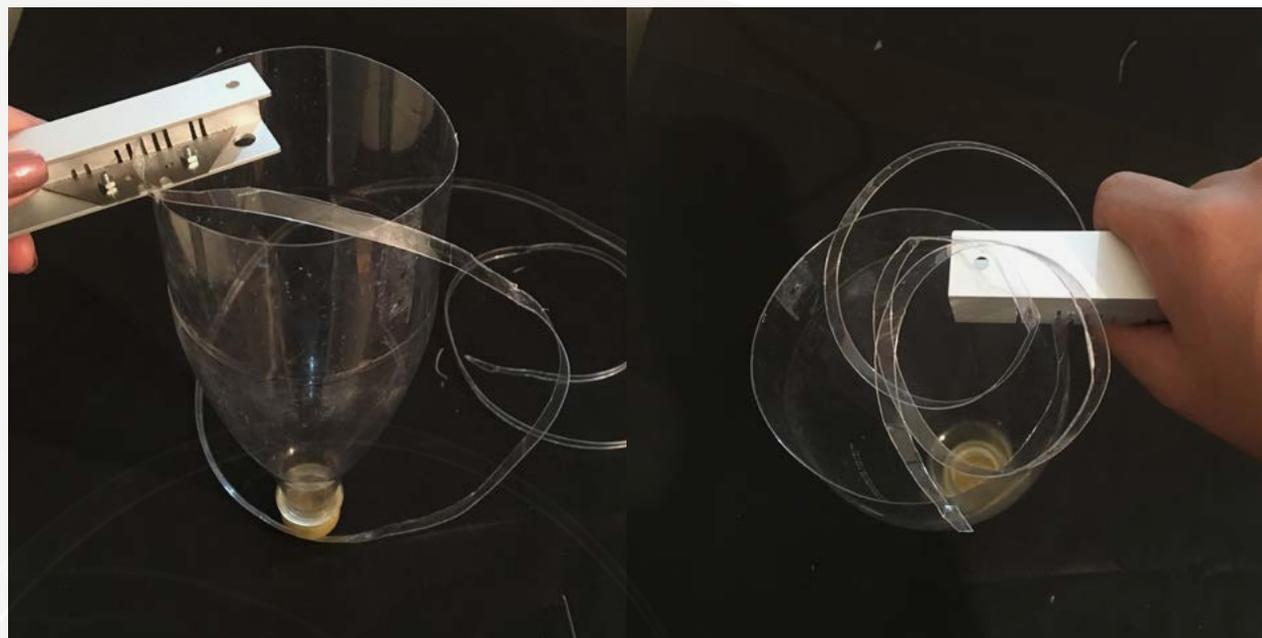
Instrumento para sacar tiras plásticas. -Fuente: Autoría propia
